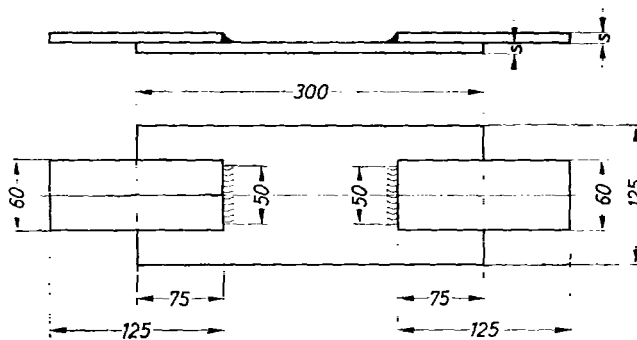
Überlapp-Prüfstück für Blechschweißer an $s = 1,5$ bis 2 mm
